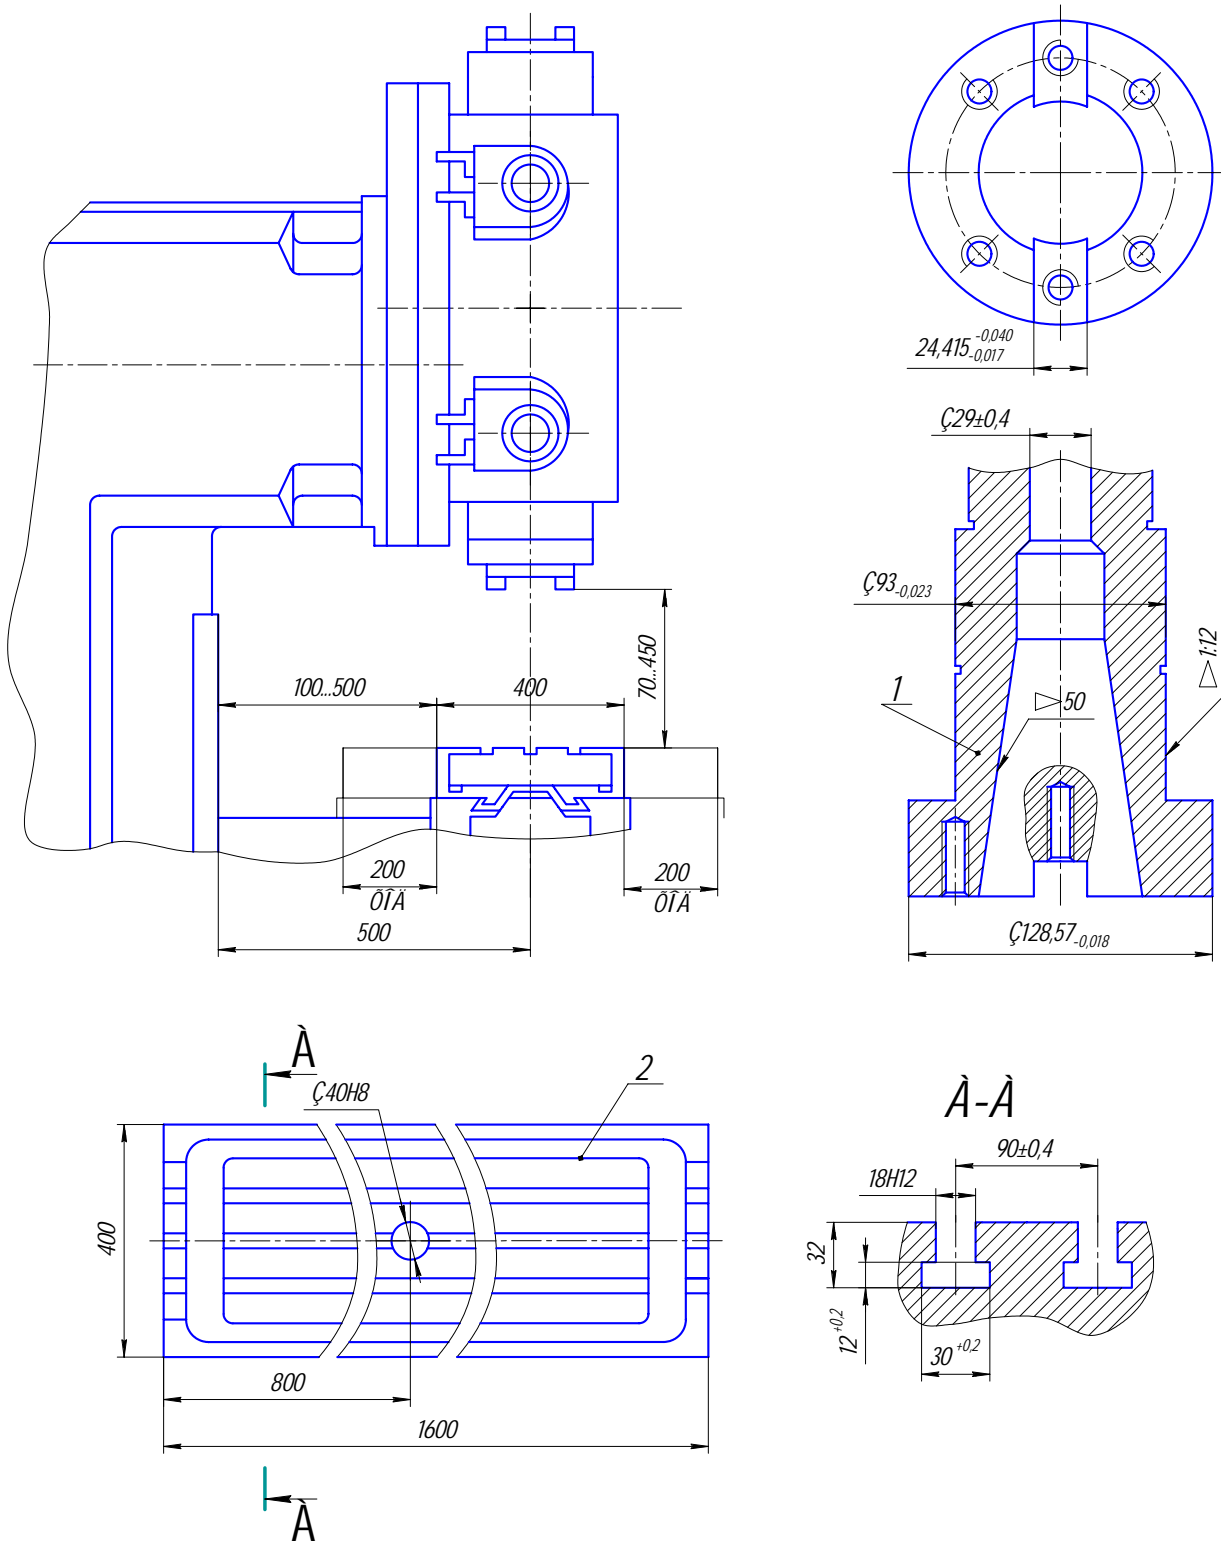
Габарити робочої зони і установочні бази вертикально-фрезерного верстата з ЧПК моделі 6P13Ф3:
